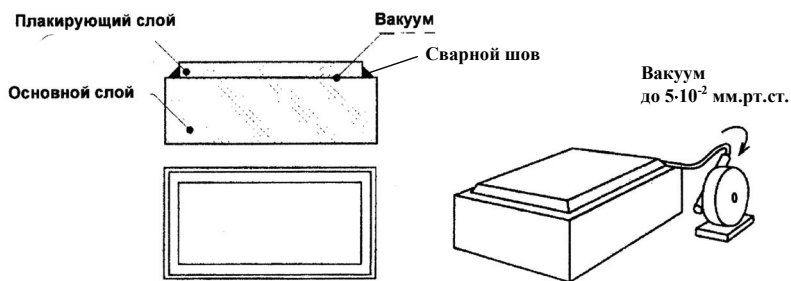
Схема сборки, сварки и вакуумирования пакета
